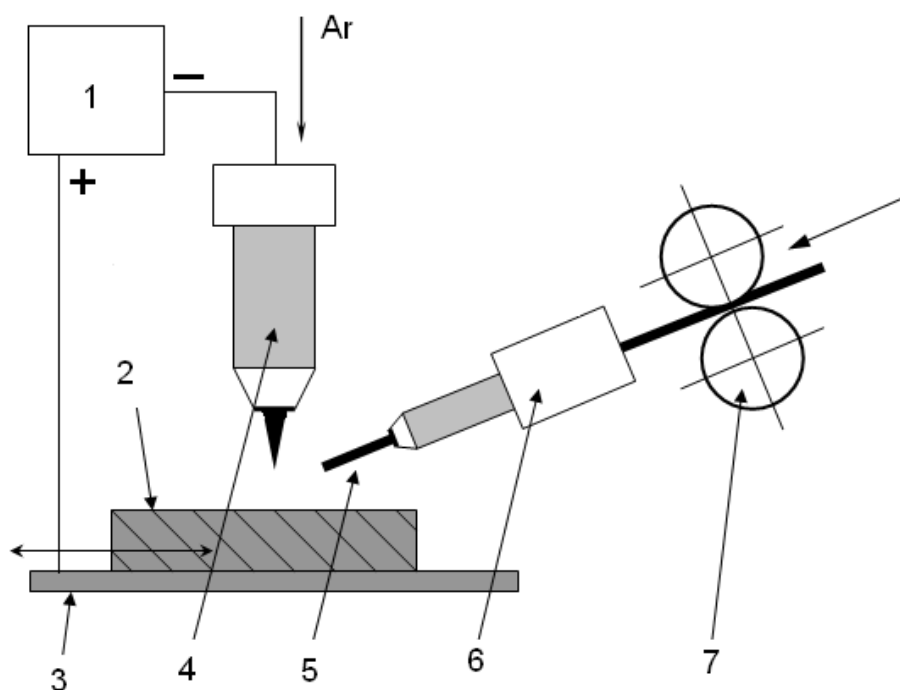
Схема наплавки дугой с неплавящимся электродом присадочной проволокой в защитной среде: 1– источник питания; 2 – изделие; 3 – подвижный стол; 4 – горелка; 5 – проволока; 6 – муштук; 7 – подающие ролики.
